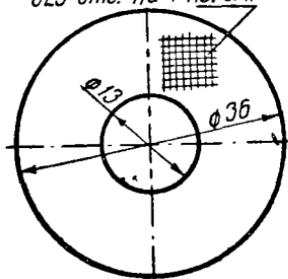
Дет. № 330. Сетка корпуса фильтра для топлива и воды
